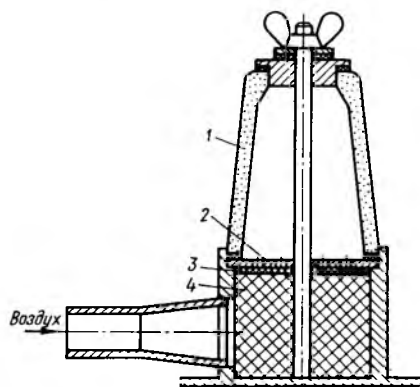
Глушитель выхлопа пневмопривода перемещения электродов одноточечных сварочных машин
